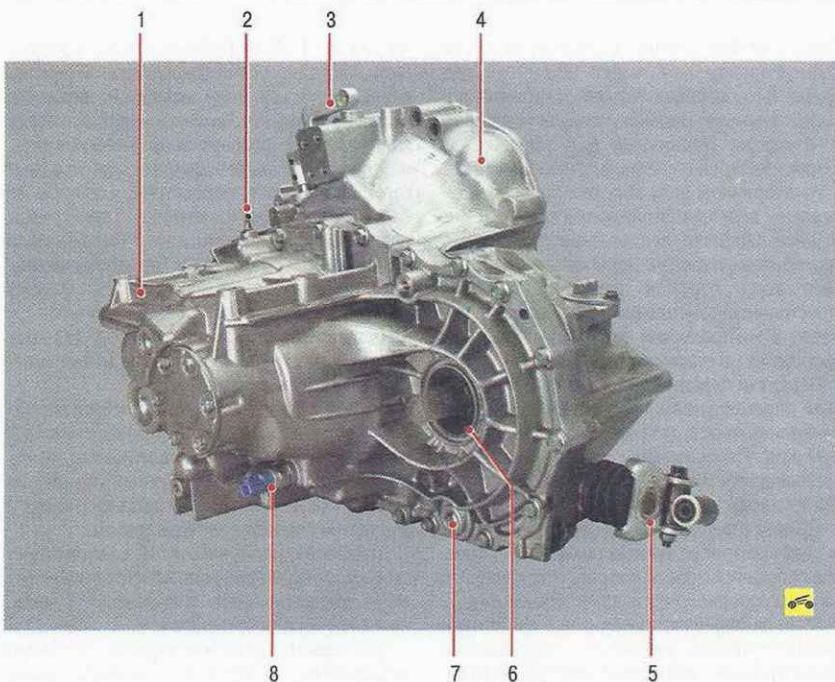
Пятиступенчатая механическая коробка передач RS5F30A: 1 – картер коробки передач; 2 – сапун; 3 – рычаг вилки выключения сцепления; 4 – картер сцепления; 5 – механизм выбора передач; 6 – сальник полуоси; 7 – пробка отверстия для слива масла; 8 – датчик нейтрального положения передач
